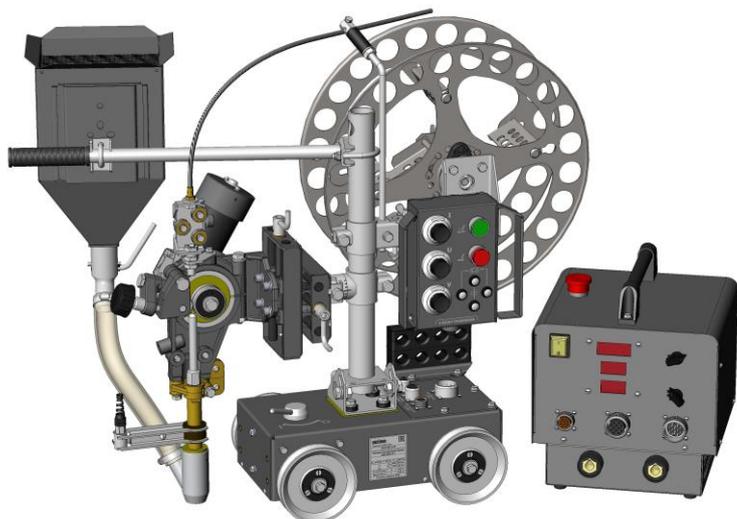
Автомат сварочный АДФ-1000-А исп.02
